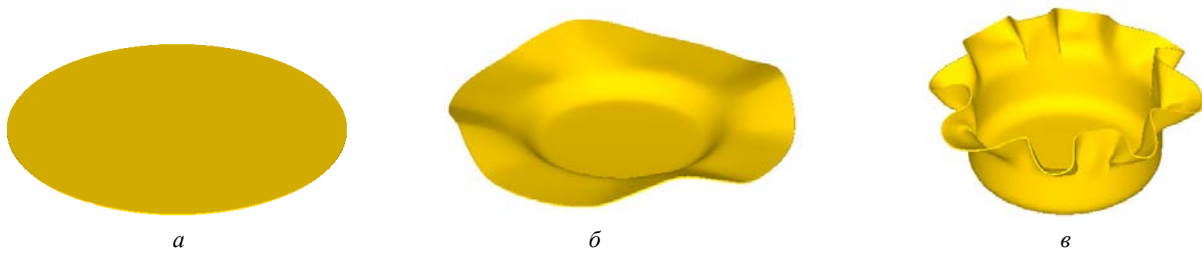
Заготовка на різних етапах першої витяжки без притискання фланця заготовки: а – заготовка, б – початок утворення гофр, в – зтягування гофр в робочу зону матриці
